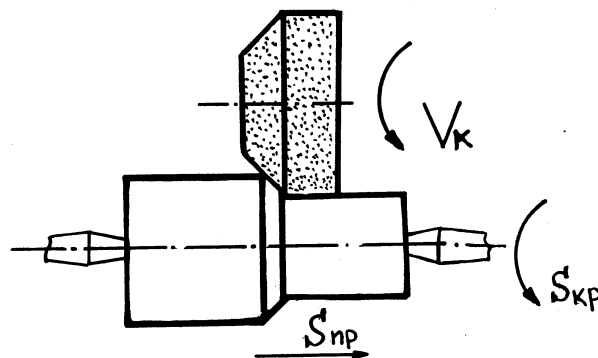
Схема глубинного шлифования цилиндрических поверхностей
